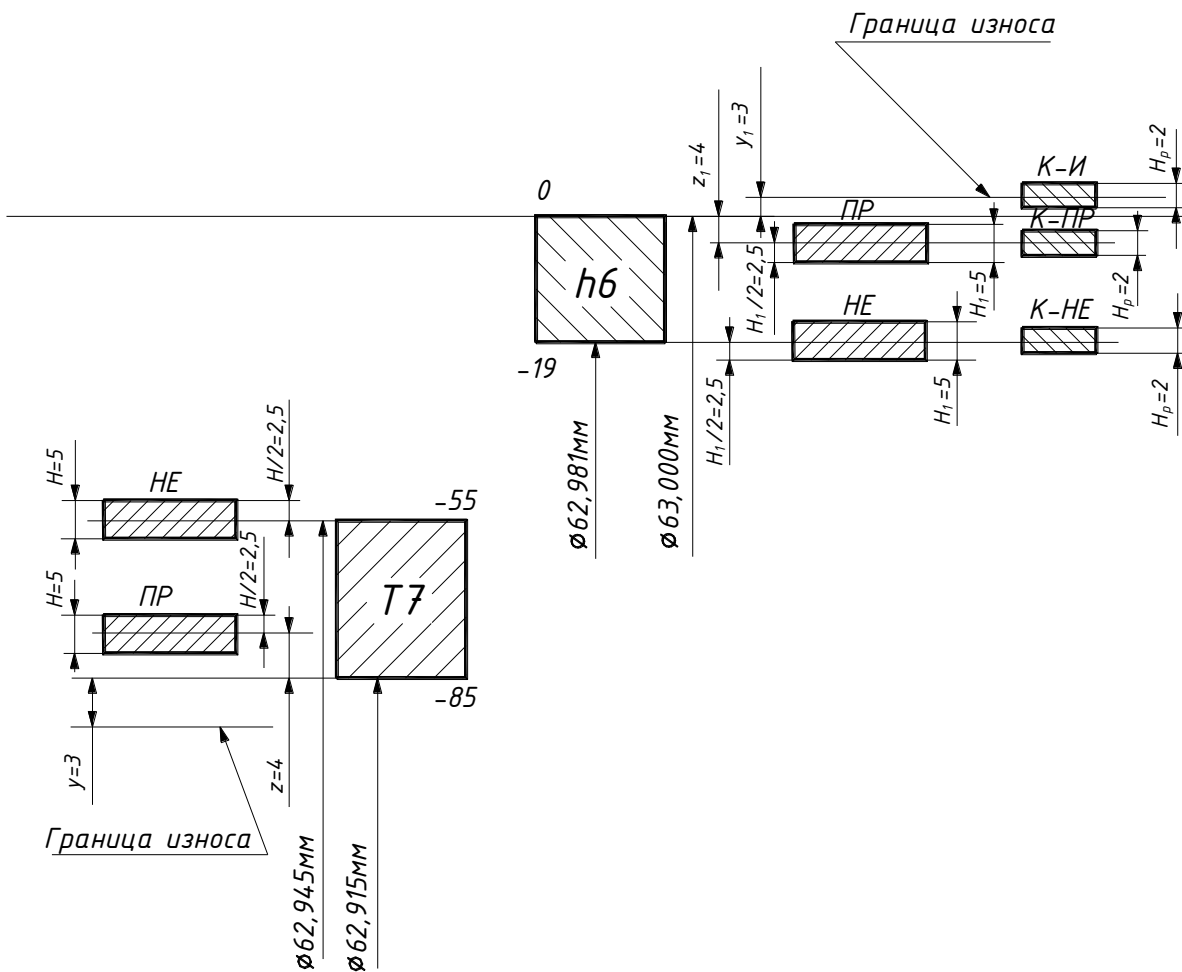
Схема розташування полів допусків деталей, калібрів і контркалібрів для посадки $\varnothing 63$ T7/h6
